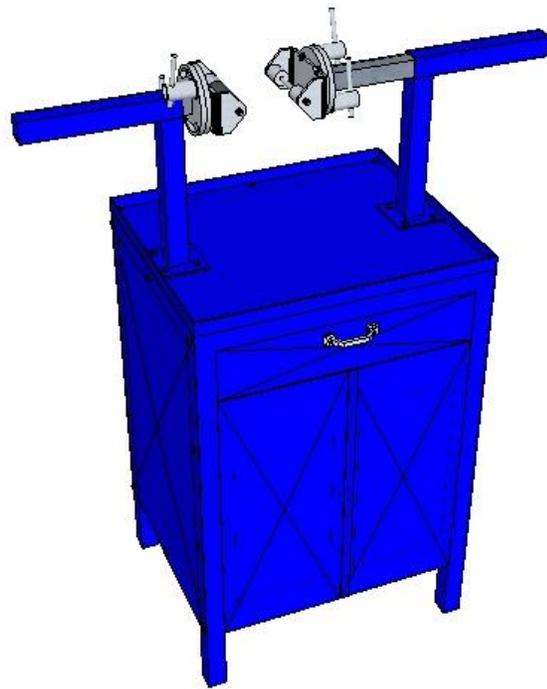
Fotografía y diseño propiedad del creador que muestra la pieza final y presentación en 3D.
